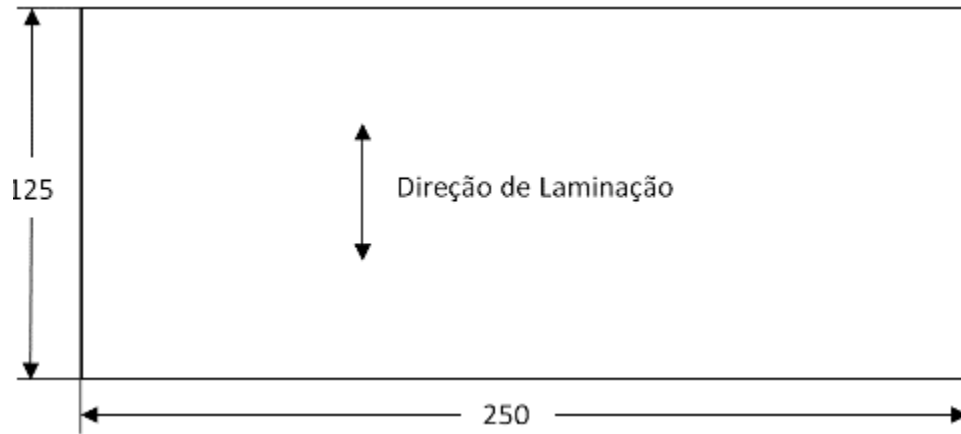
Dimensões do corpo de prova para confecção das juntas soldadas.
